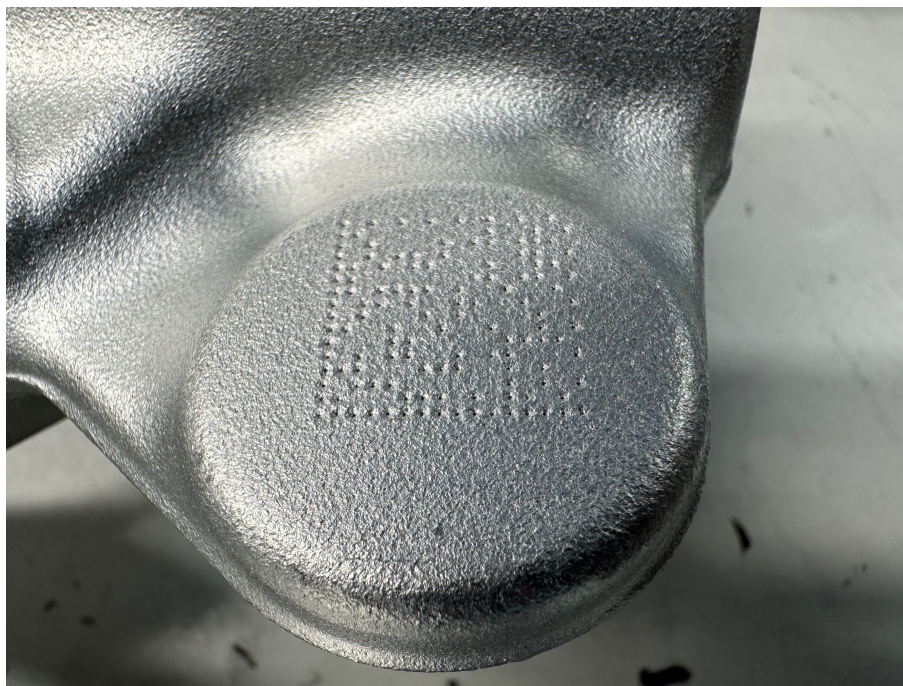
makro sken s měřením v 2. směru (lesklý)
